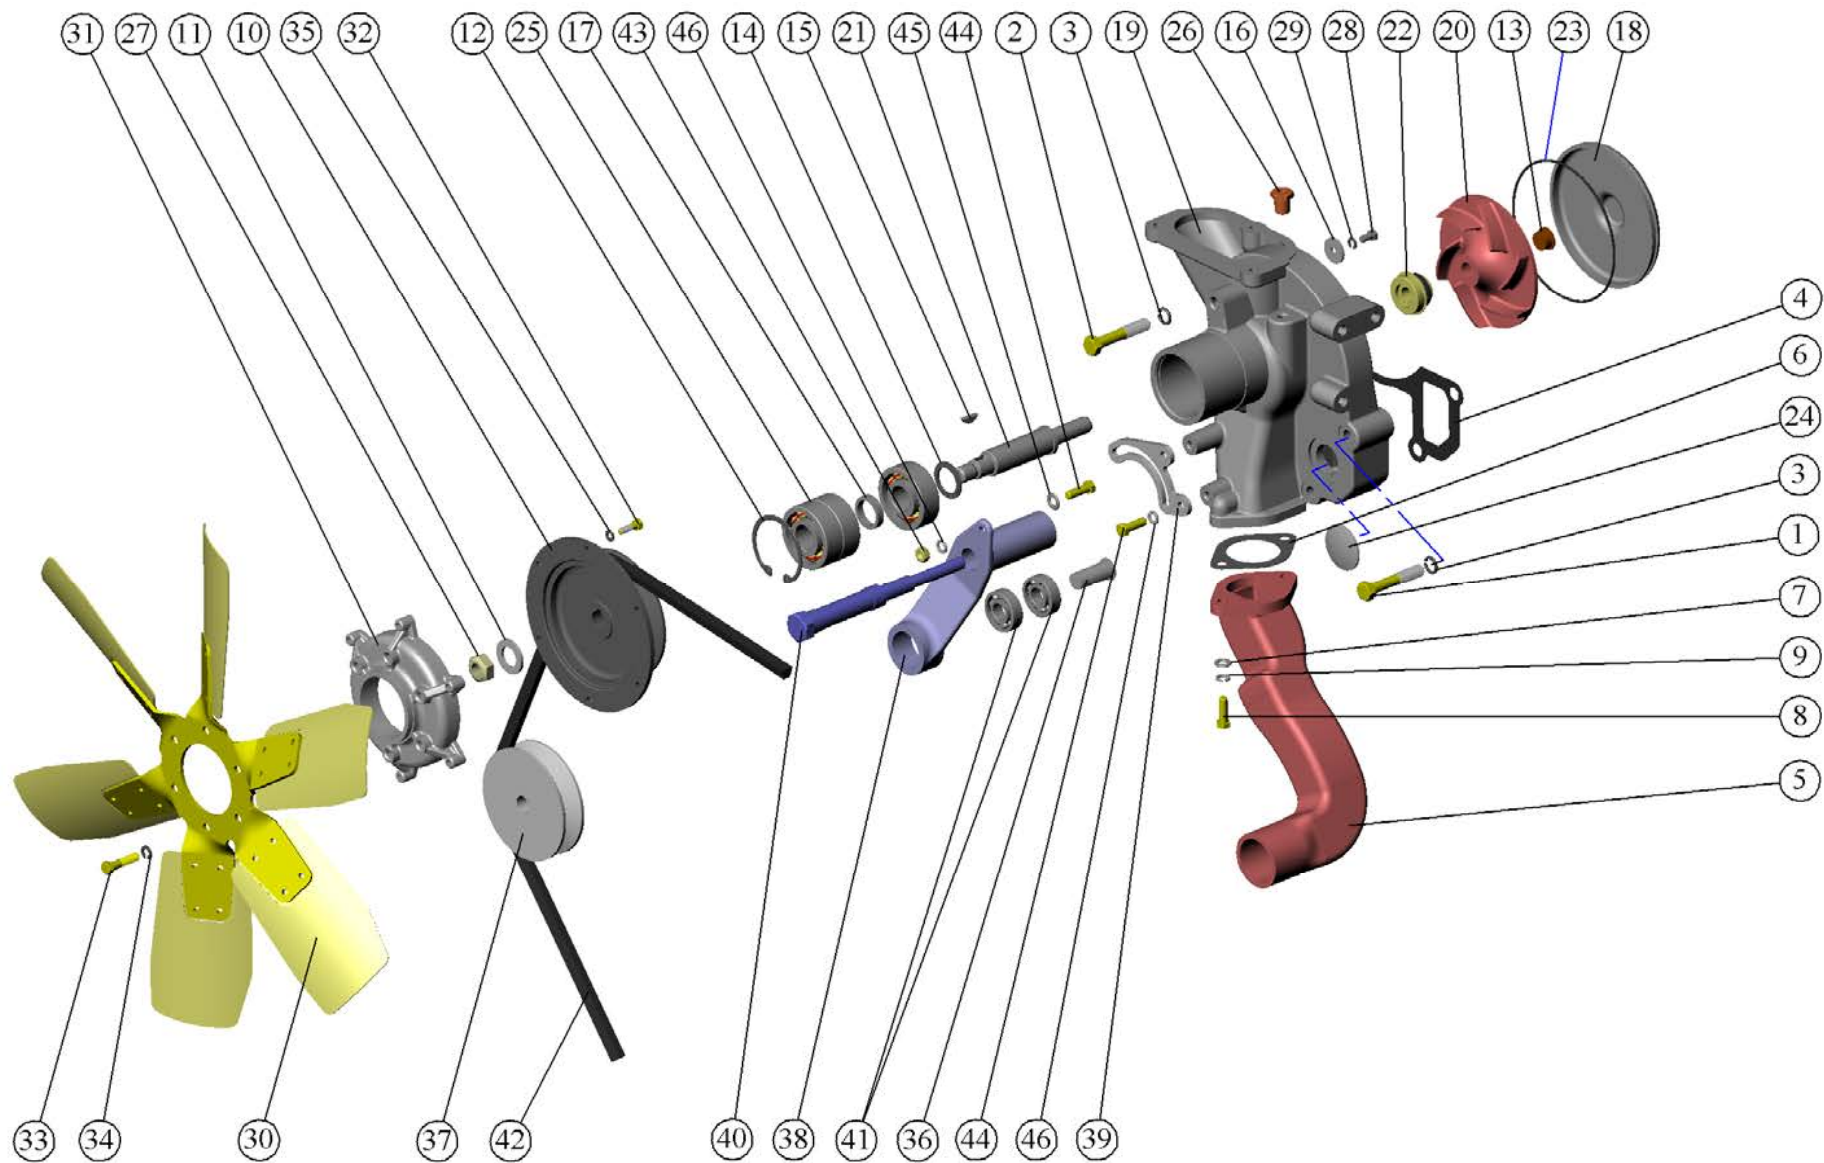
Насос водяной. Установка вентилятора. Установка натяжителя.
